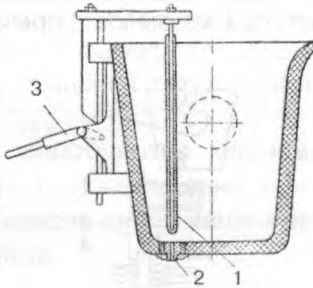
Ливарний ківш для розливки сталі: 1 - стопор; 2 - стакан; 3 - стопорний механізм
